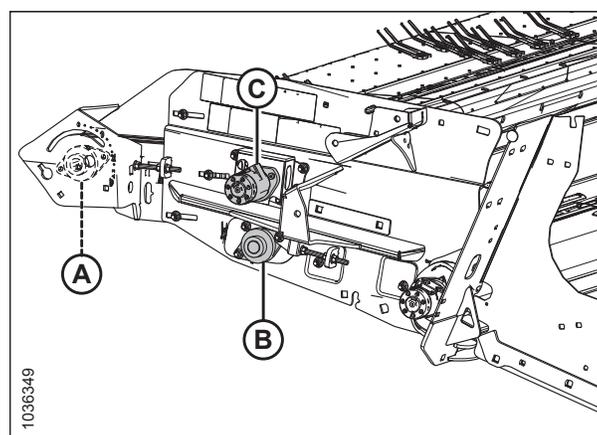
Rodamientos con accesorios de engrase: lado izquierdo de la plataforma
